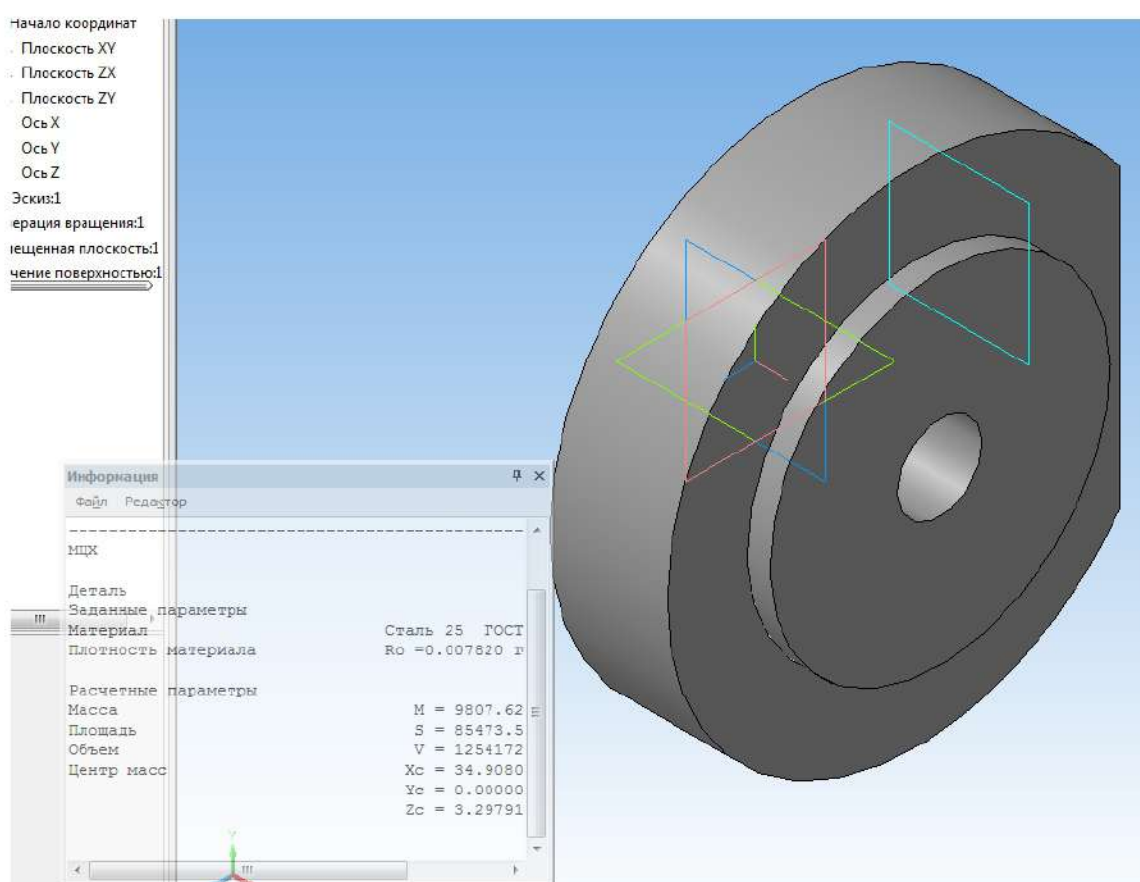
Виготовлення заготовки литтям в піщано-глинисті форми
